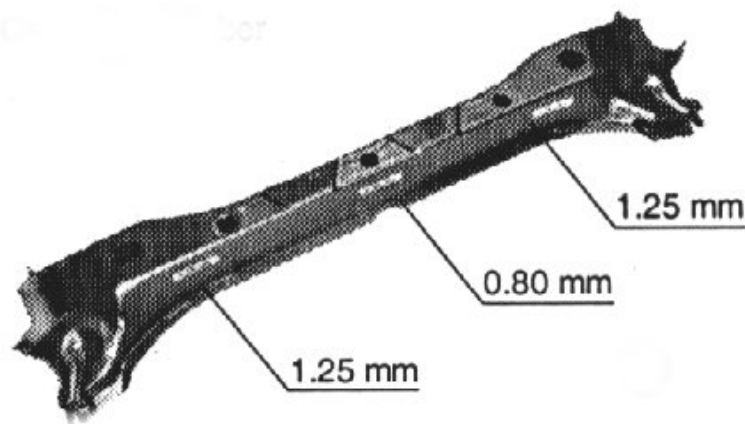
Barra transversal de um componente automotivo produzido por laminação flexível /2.2/.
